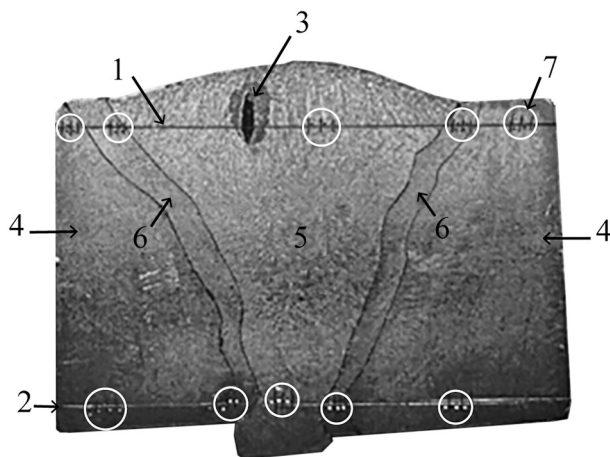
Общий вид металлографического шлифа сварного соединения из стали 10ХСНД в исходном состоянии с расположением зон сварки, линий и точек замеров микротвердости: 1, 2 — линии замеров микротвердости; 3 — несплавление; 4 — основной металл; 5 — сварной шов; 6 — зона термического влияния; 7 — точки замеров микротвердости
